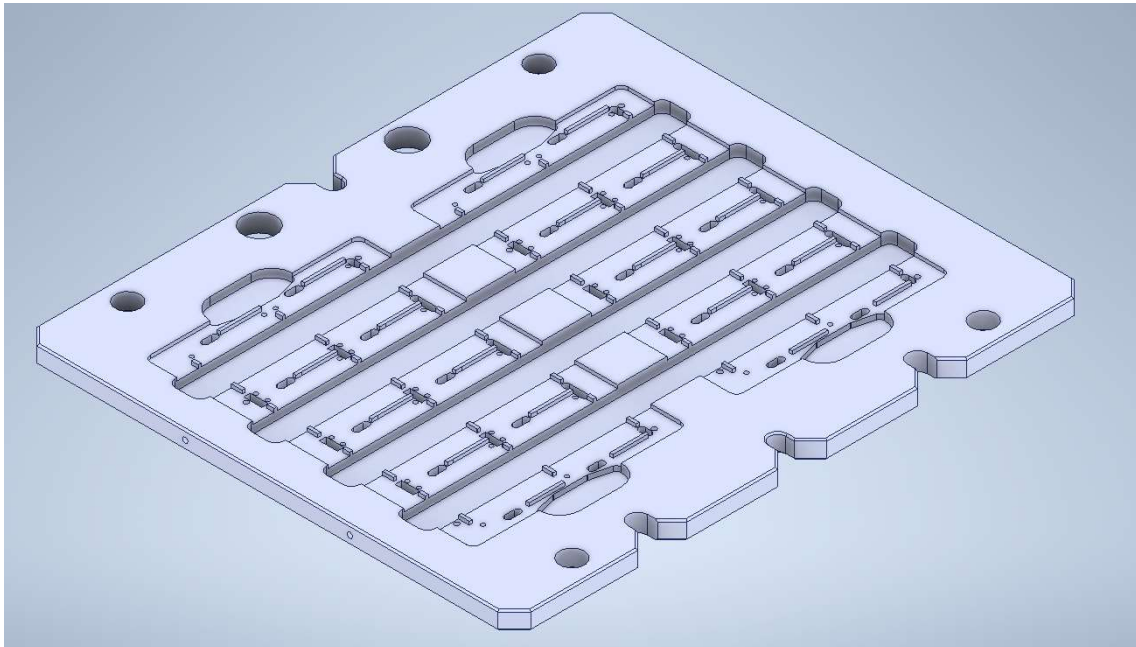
Fixační přípravek [zdroj - vlastní]
